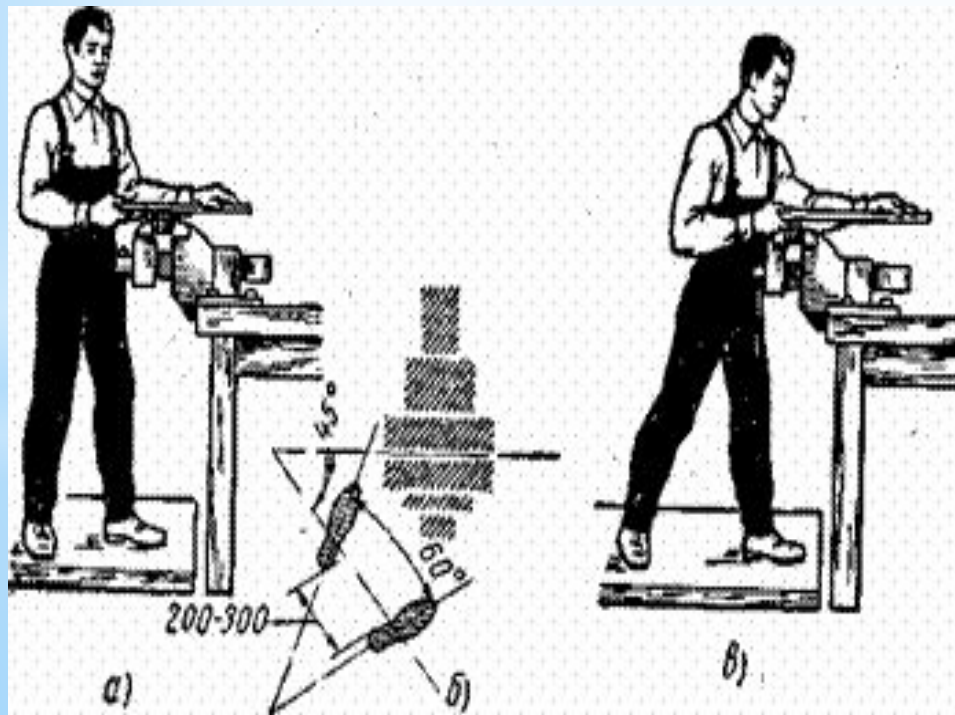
Положение рабочего у тисков: а — положение корпуса, б — схема расположения ног, в — положение корпуса при грубом опиловании
